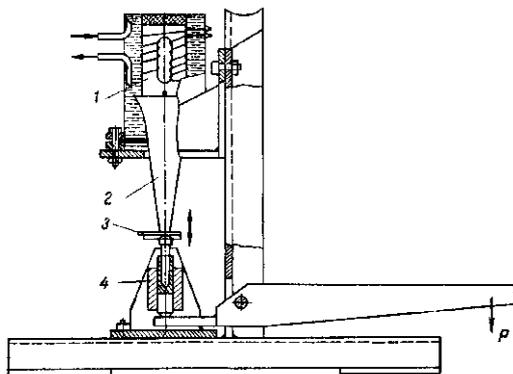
Схема ультразвуковой сварки пластмасс:
